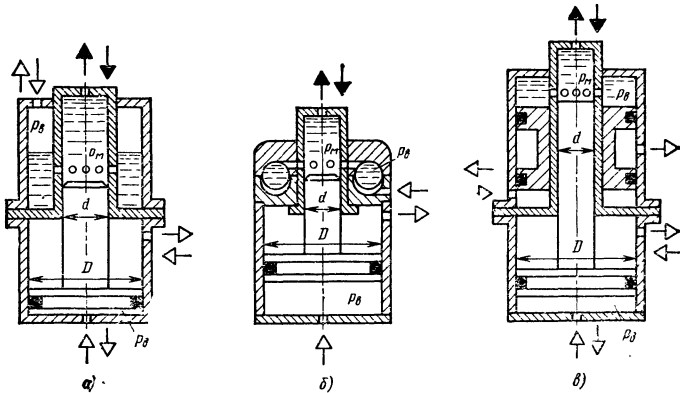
Схемы двухступенчатых пневмогидропреобразователей:
